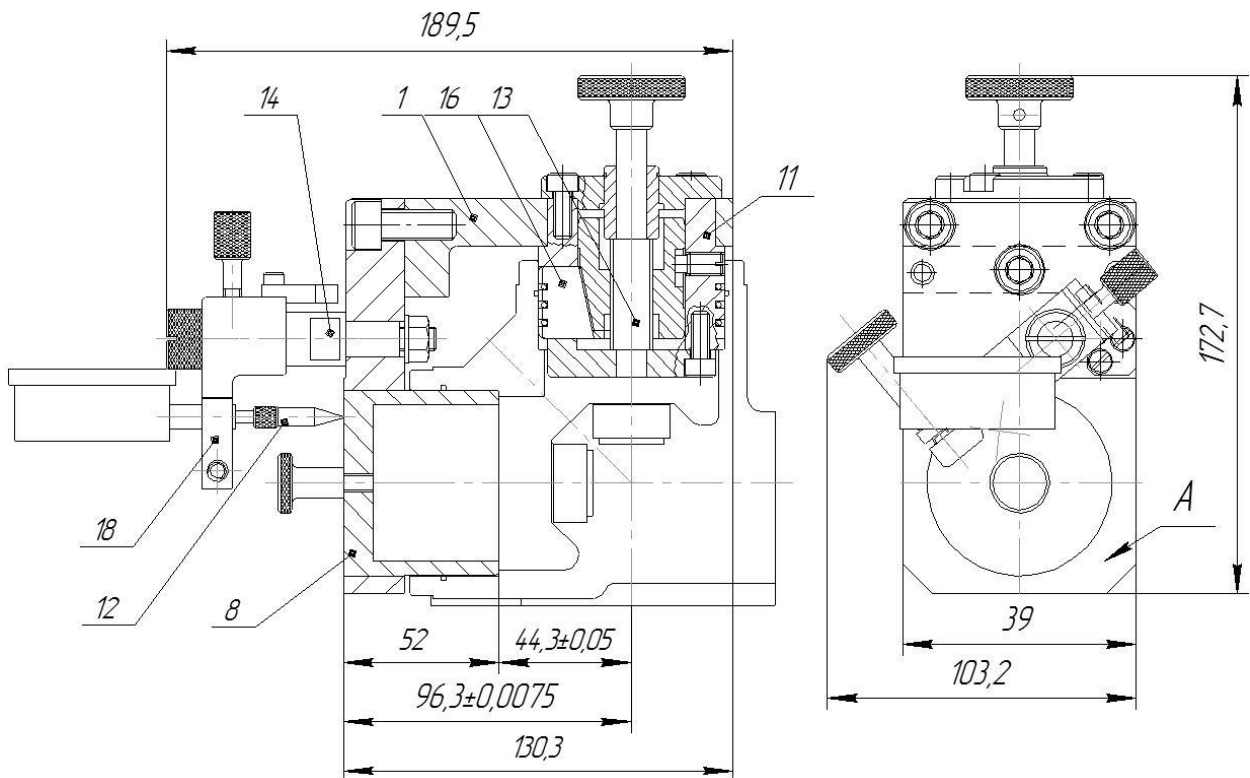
Конструкція контрольно-вимірювального пристрою:
